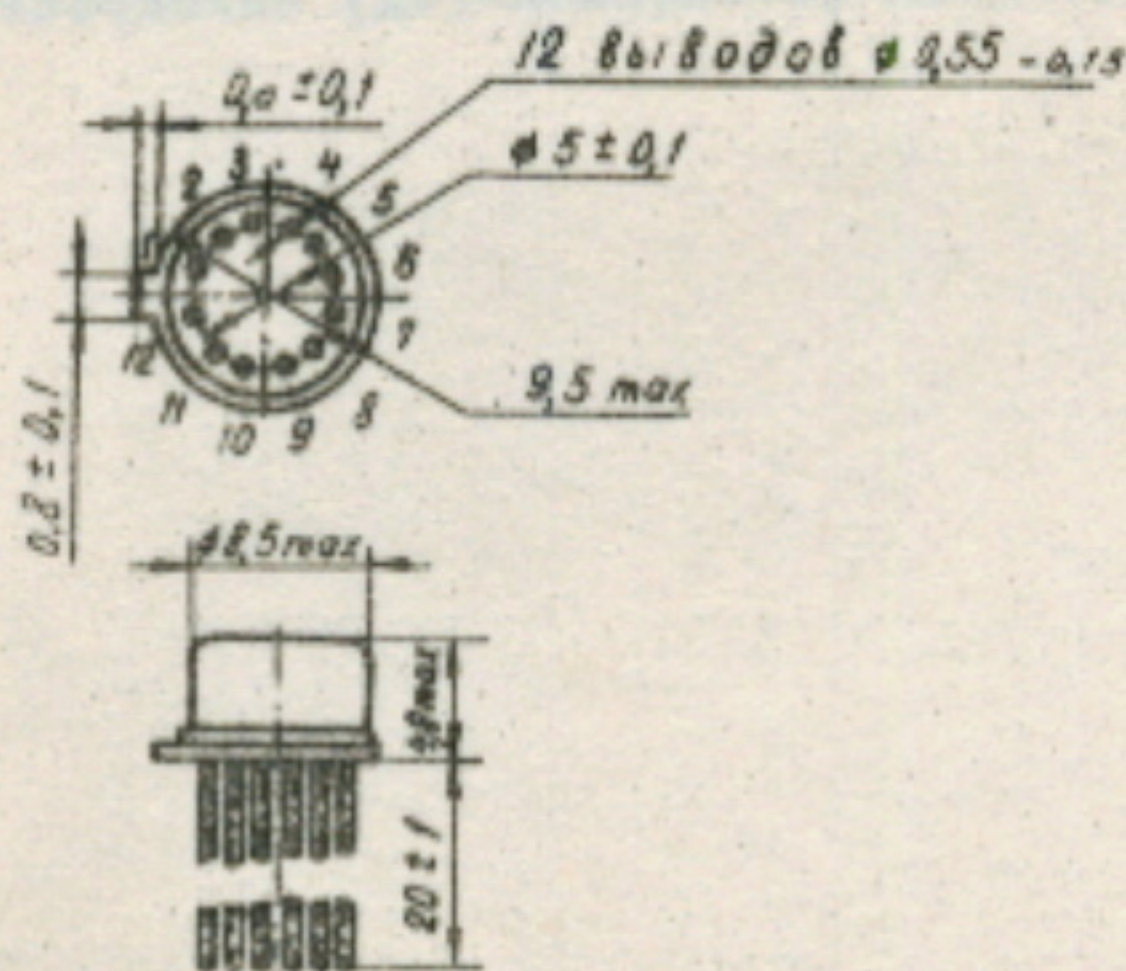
Габаритный чертеж корпуса 30I.I2-I
